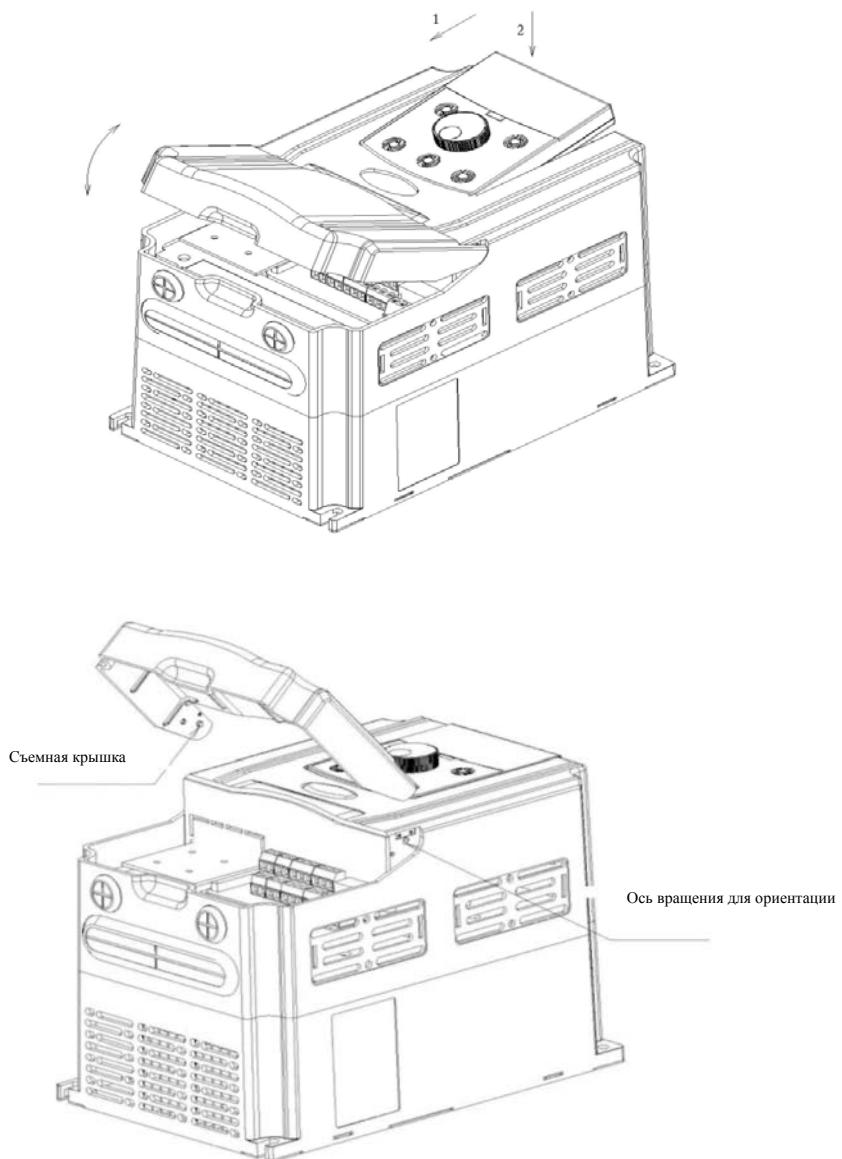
Снятие верхней крышки пластмассового кожуха
